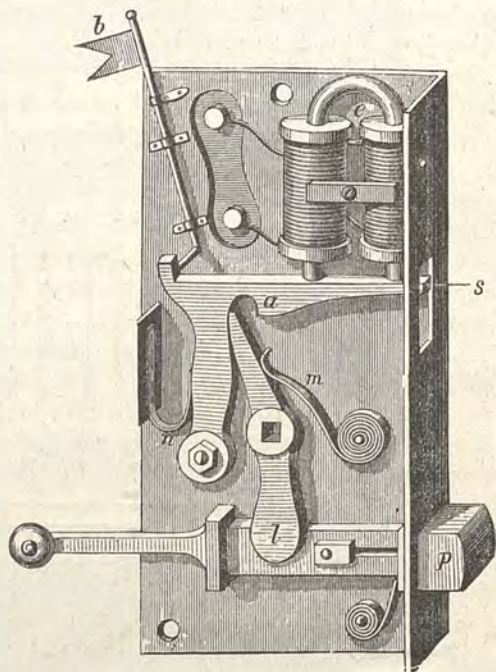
Serratura elettrica Meardi-Zelaschi.
